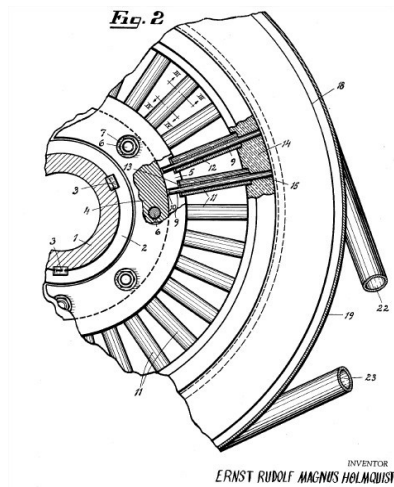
Dessin du rotor *Axial Flow Gas Turbine* inventé par Holmquist (vue de face)
